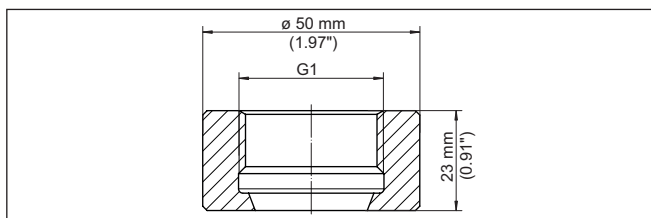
Dimensions raccord à souder direct G1 (ISO 228-1) - joint conique
